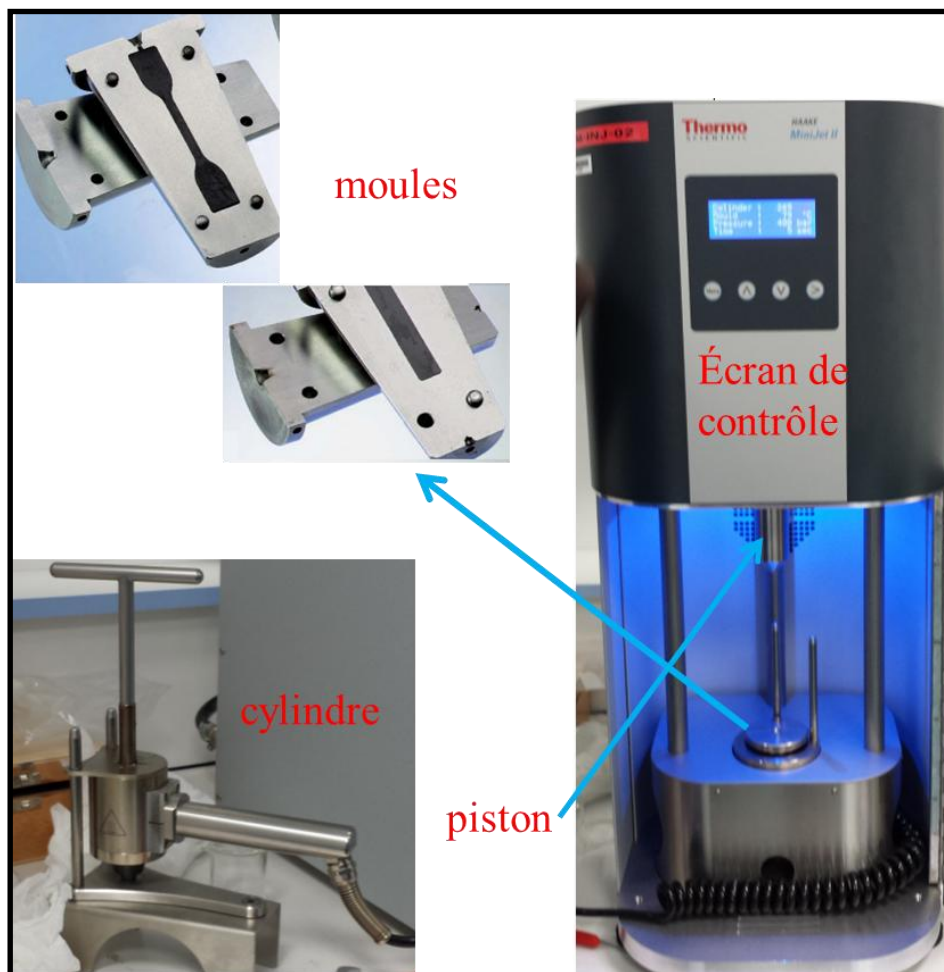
Mouleuse par injection « Thermo scientific HAAKE Minijet II »
